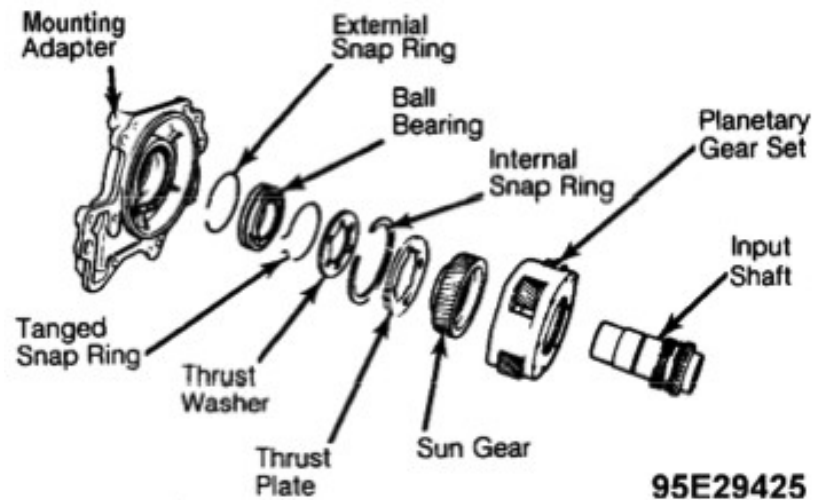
vista explodida do conjunto de engrenagens planetárias.
